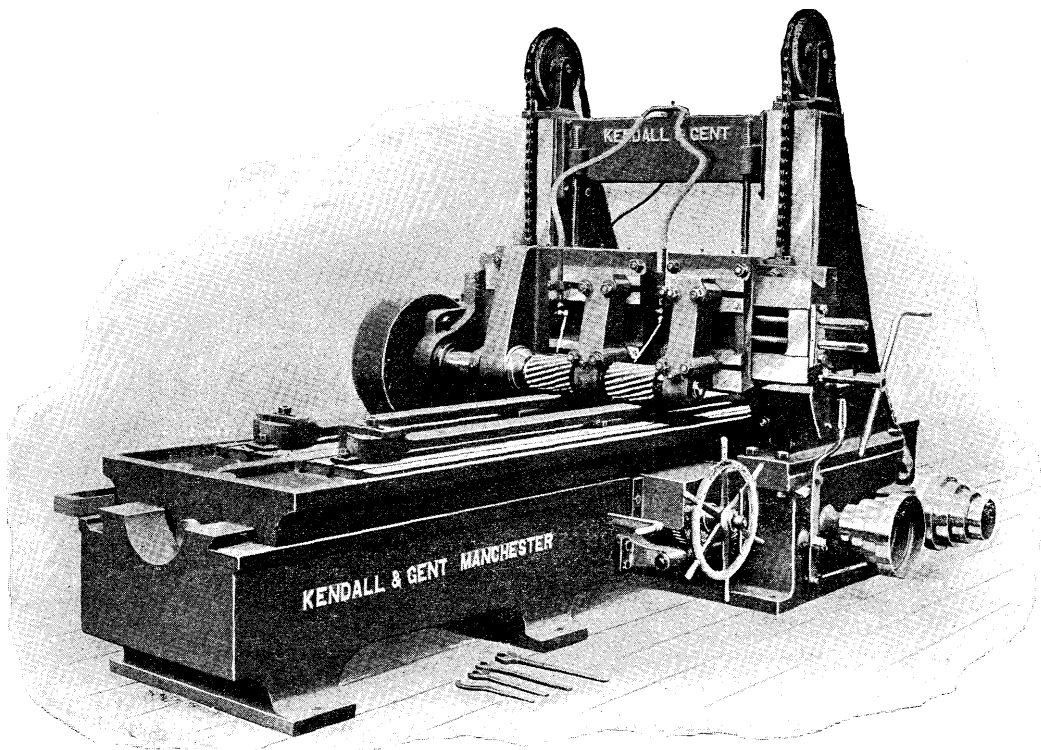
Fraiseuse-raboteuse à fraises horizontales, de MM. Kendall et Gent, de Manchester.
